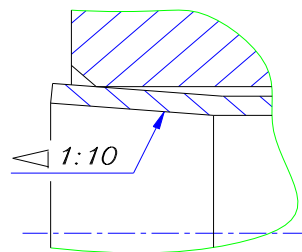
Конічне розвальцьовування труби перед зварюванням
